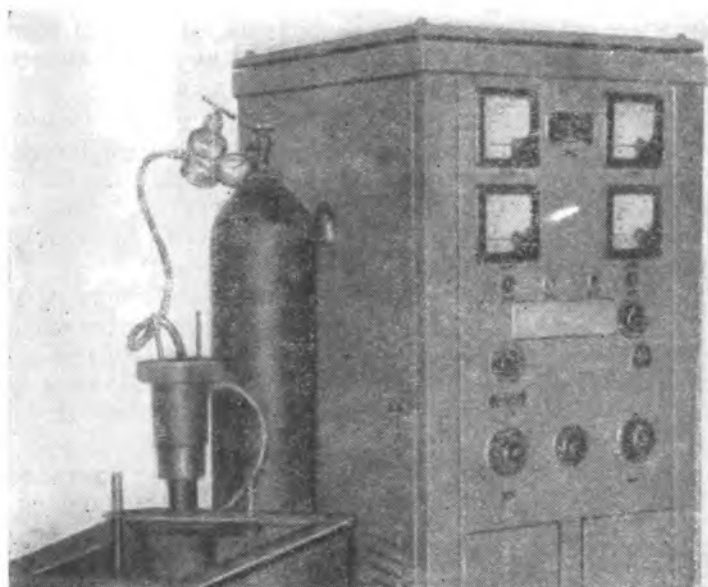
Силовая ультразвуковая установка для обработки заготовок режущих инструментов
